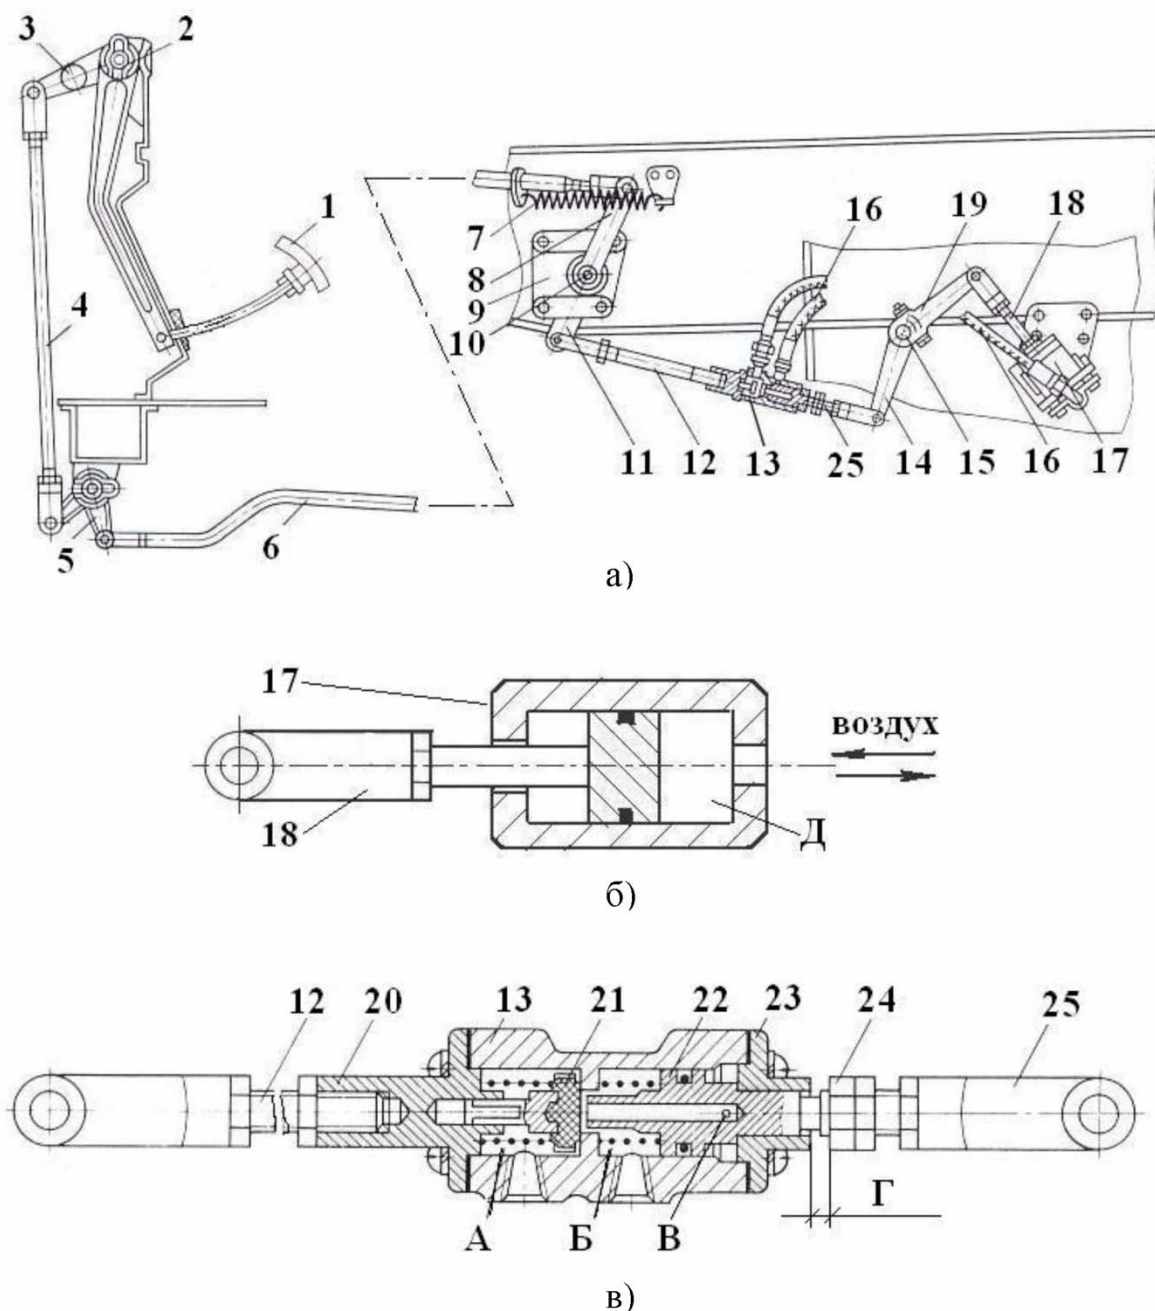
Привод выключения сцепления автомобиля МАЗ 5335 с пневматическим усилителем:
